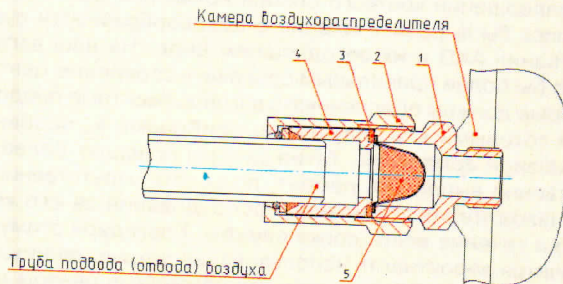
Устройство безрезьбового соединения: 1 — штуцер; 2 — накидная гайка; 3 — прокладка; 4 — ниппель; 5 — колпачок-фильтр
